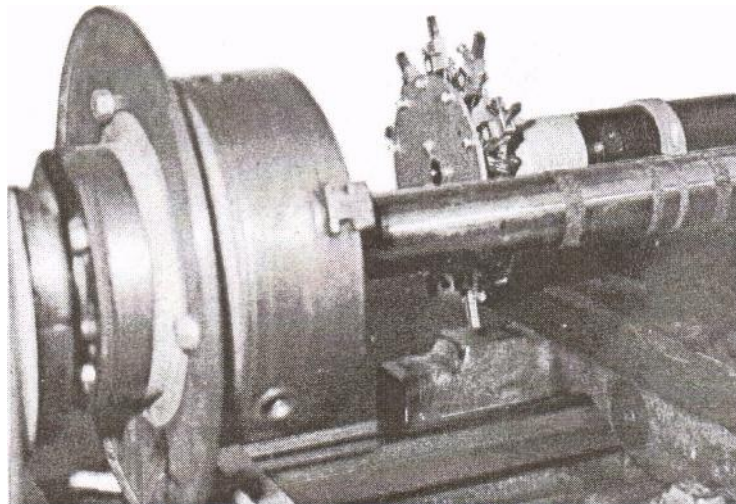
Внешний вид установки ЭЛИТРОН—347
